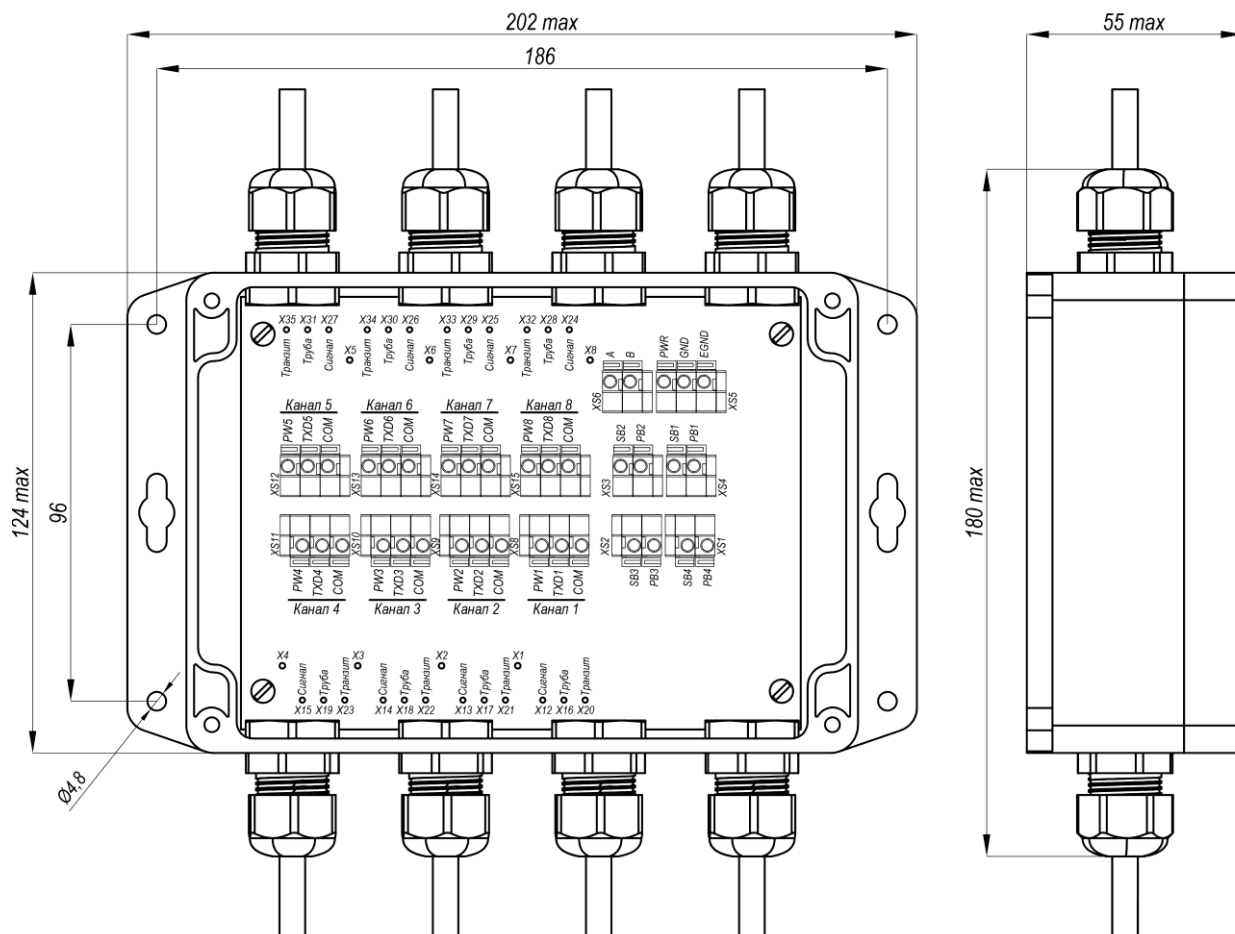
Габаритные и установочные размеры модуля Концентратор-КД2
